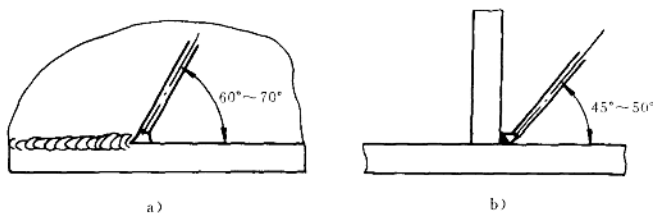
T 形接头平角焊位置焊条电弧焊施焊打底层焊条角度[⊙]
